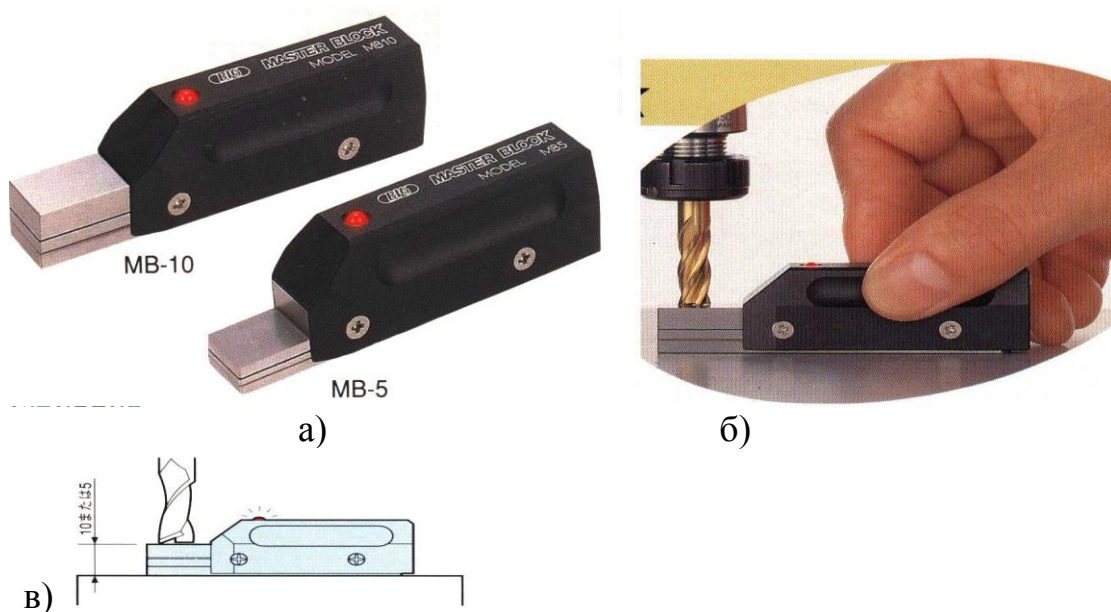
Ручний калібр «MASTER BLOCK», де а - зовнішній вигляд, б – позиціювання на верстаті, в – торкання інструмента для визначення координат
